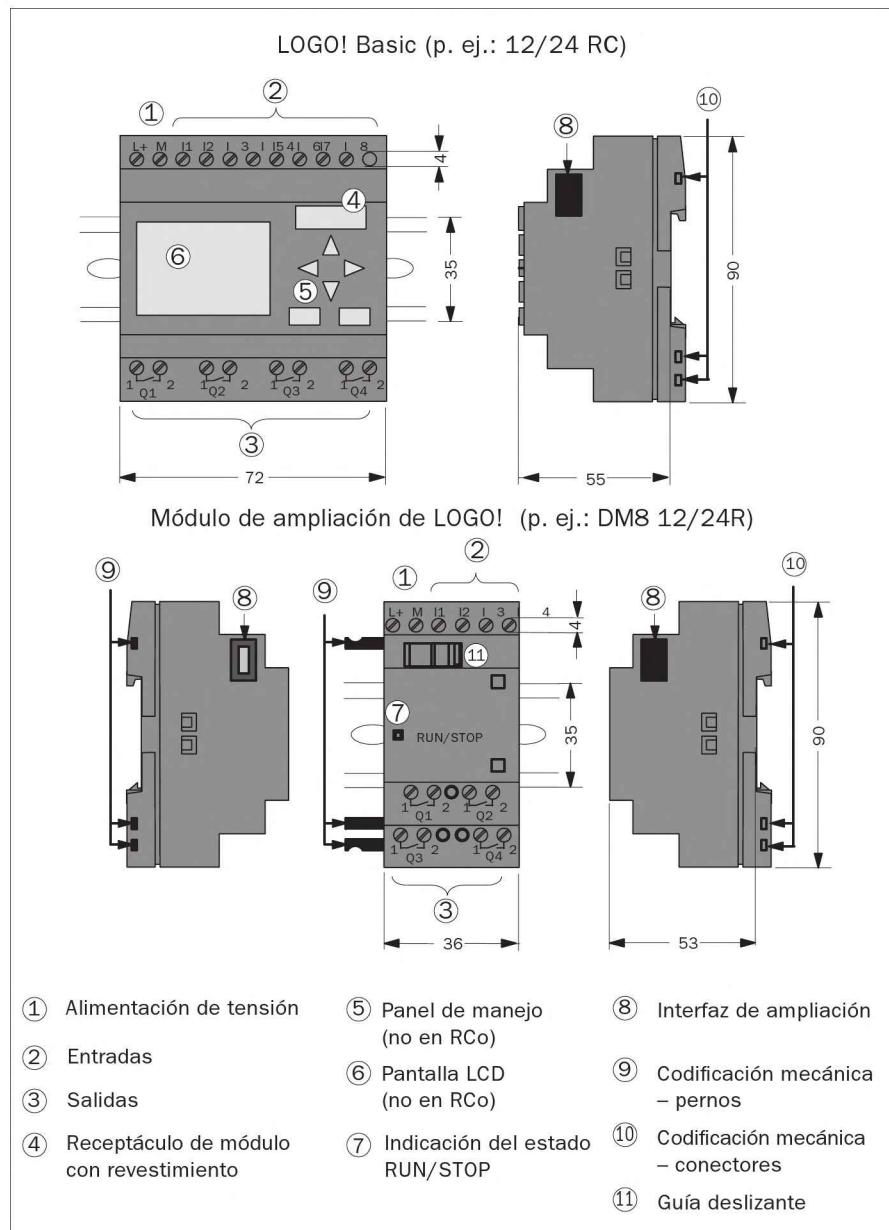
Partes y dimensiones de LOGO!. Cortesía de Siemens.
